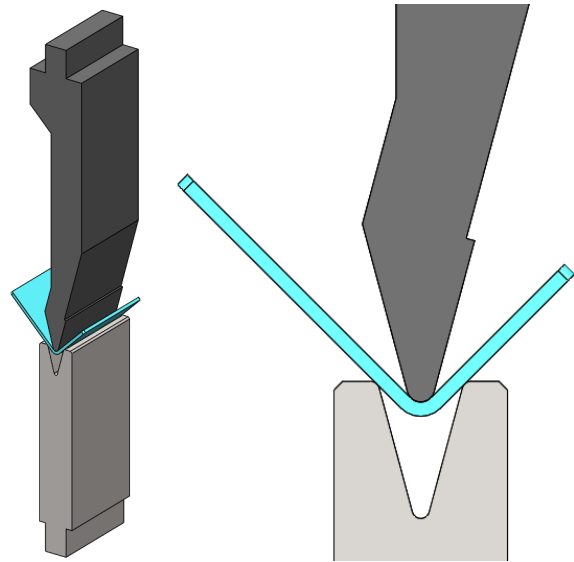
Werkzeug einer Standard-V-Abkantpresse
